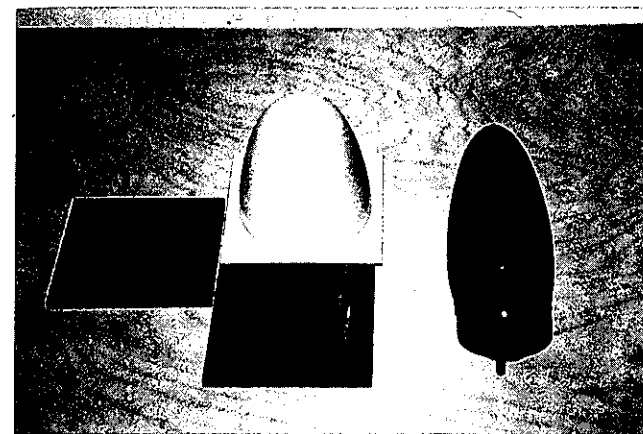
Links: Materialien zum Bau der Strömungsverkleidung der Bauer Impellerserie. Rechts: Integrierter Tank der Axiflo Impellerserie.
